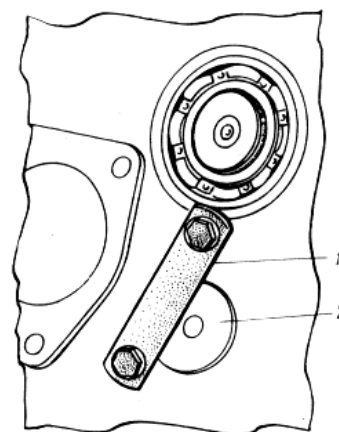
Знімання стопорної планки осі проміжної шестерні: 1- стопорна планка; 2- вісь проміжної шестерні
